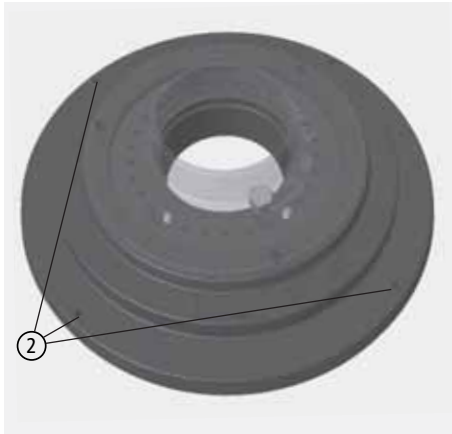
Bohrungen für Gewindestifte in Drehkonsole
